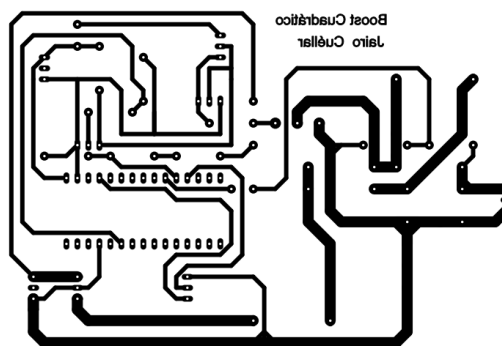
Diseño PCB Convertidor Boost cuadrático.
